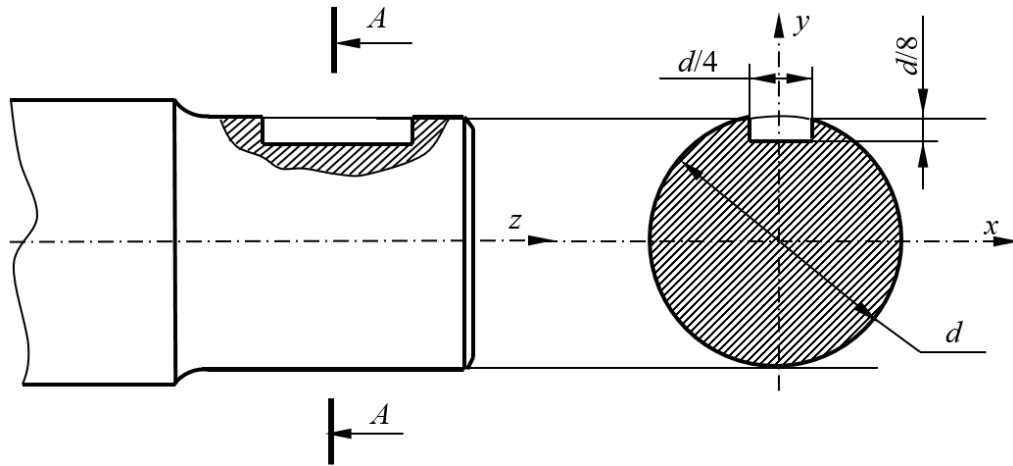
Эскиз вала со шпоночным пазом
